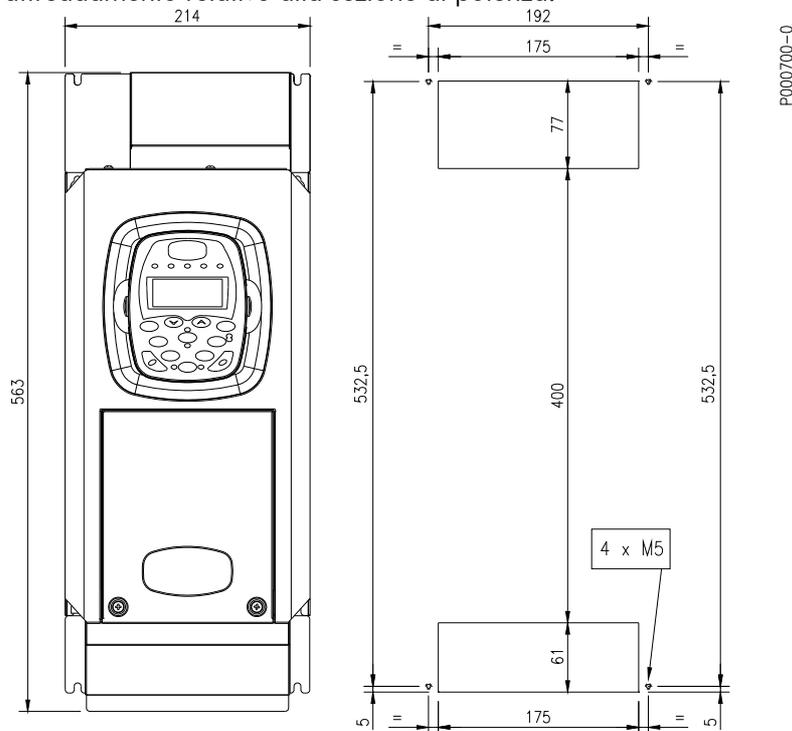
Dime di foratura del pannello per realizzare il montaggio passante SINUS K S12
